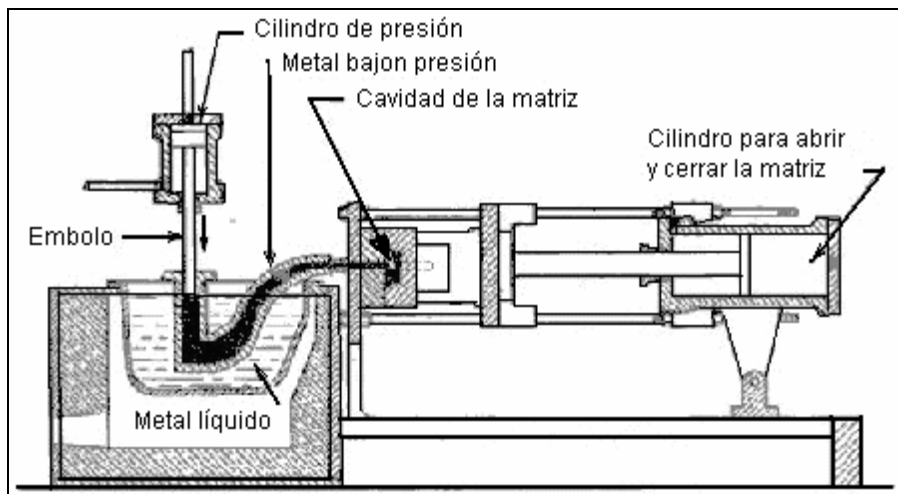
Máquina de cámara caliente para fundición en matriz
